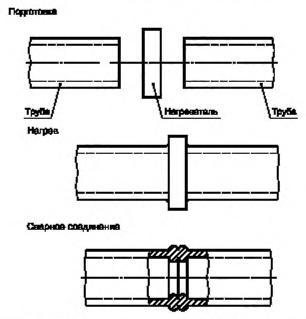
Принцип сварки встык трубы нагретым инструментом
